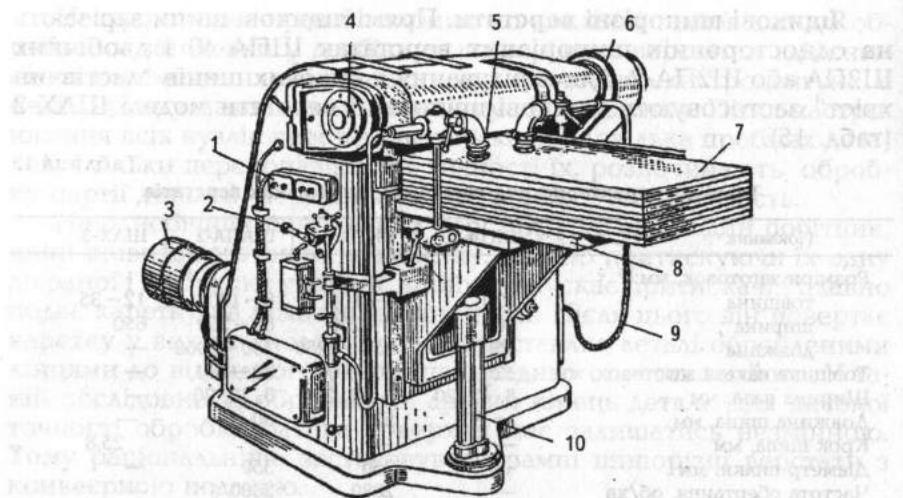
Ящиковий шипорізний верстат з автоподачею ШПА-40:
